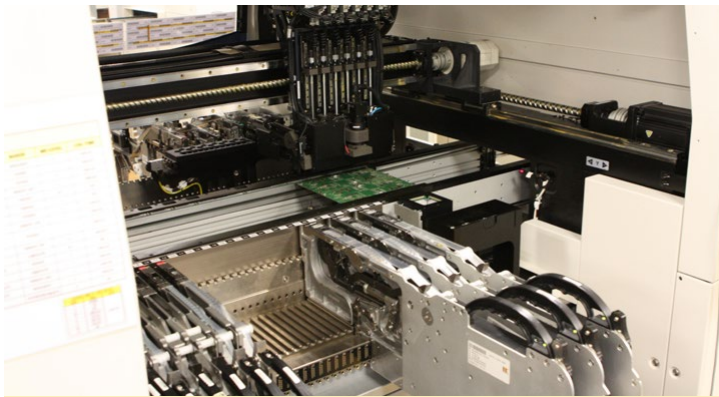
La maquina Surface Mount Technology (SMT) monta los dispositivos sobre la PCB
